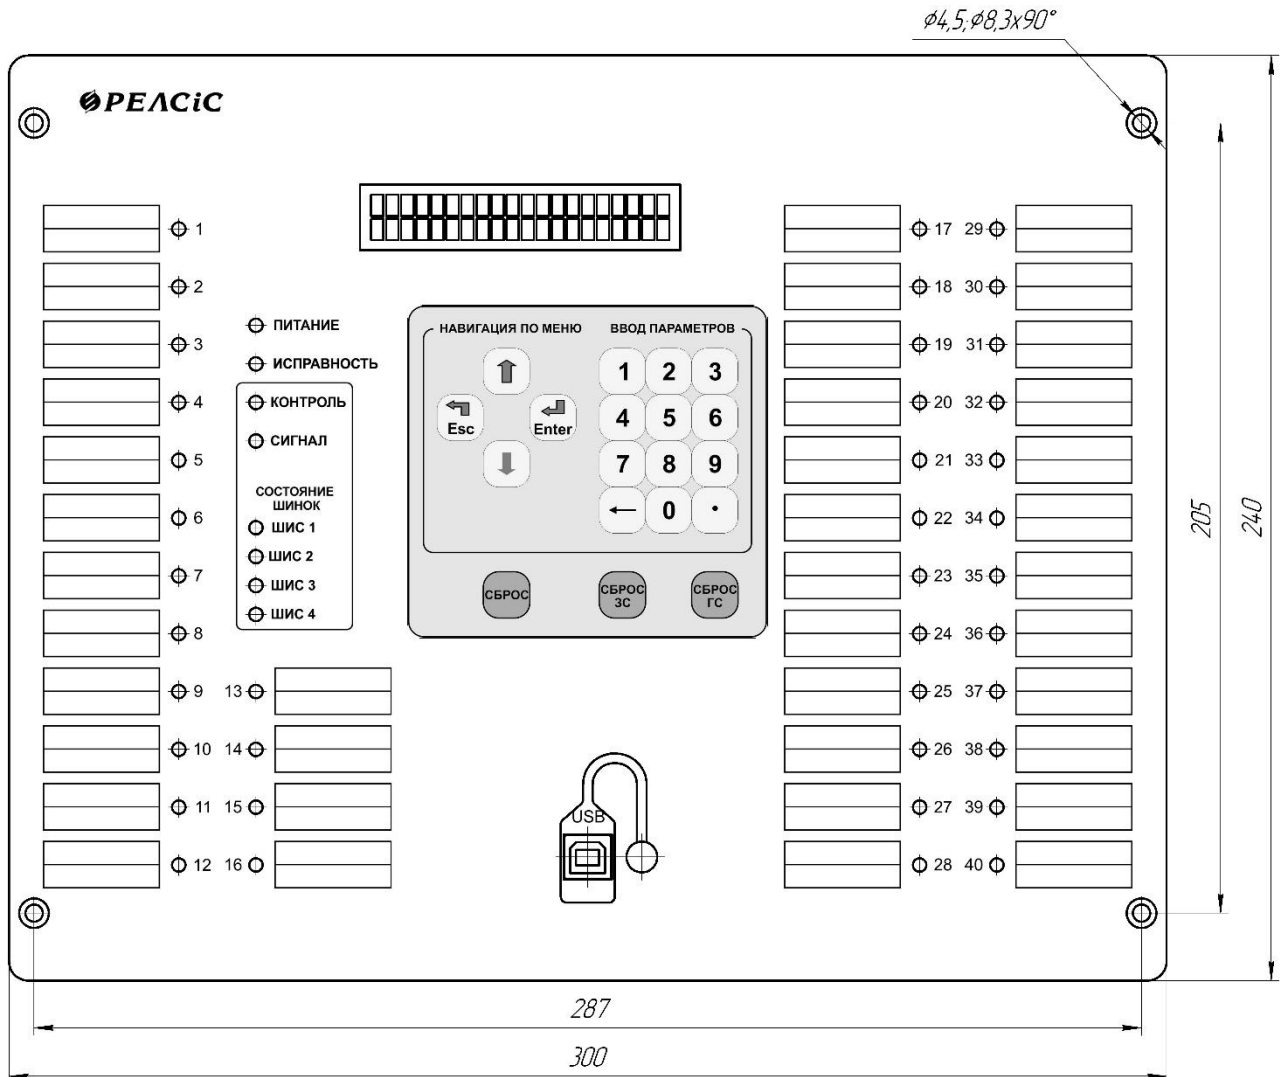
Габаритные размеры и установочные размеры и внешний вид передней панели устройства РЗЛ-05.Ш1 ЦС
